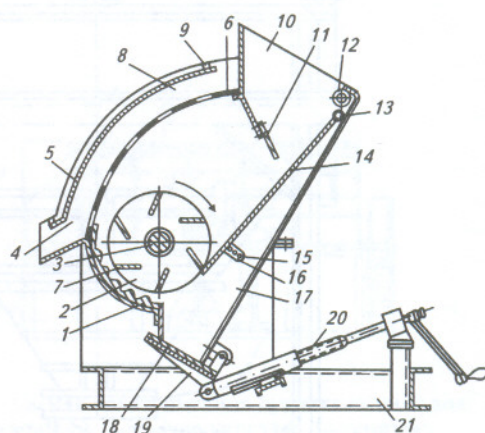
Схема фрезерно-струминного млина ФСМ-3:
